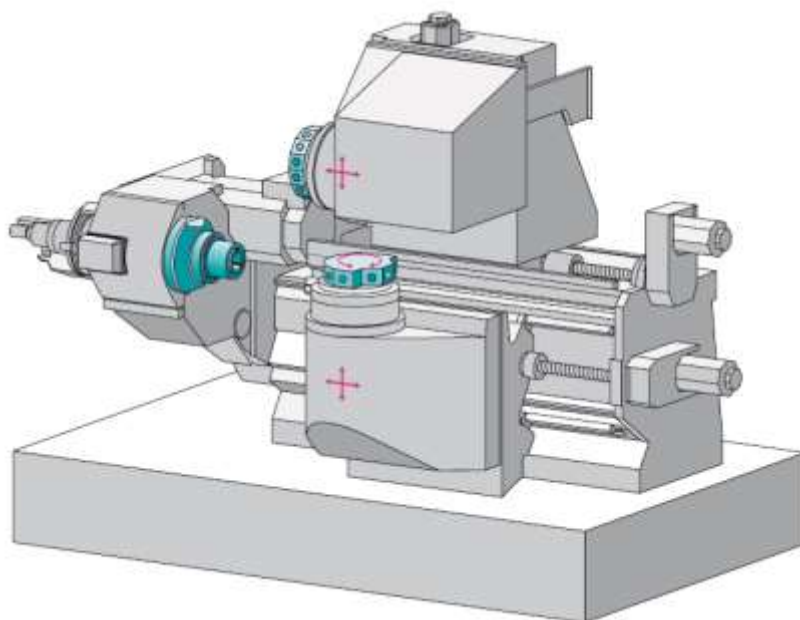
Компоновка токарного верстата з ЧПК мод. IT600 фірми INDEX для багатоінструментальної обробки
